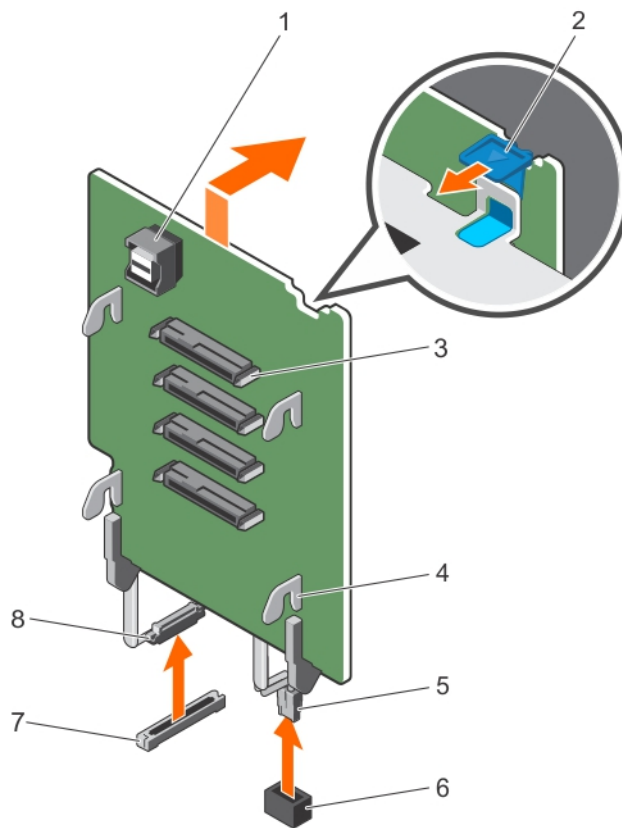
Extracción del plano posterior SAS/SATA (x4) de 2,5 pulgadas
